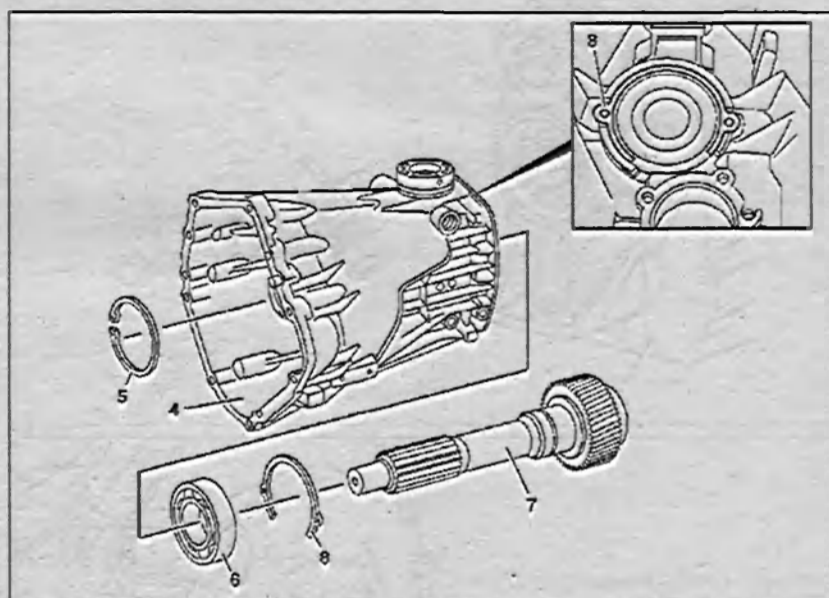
Снятие и установка первичного вала: 4 – Передняя часть корпуса МКПП; 5, 8 – Стопорные кольца; 6 – Шарикоподшипник; 7 – Первичный вал.
